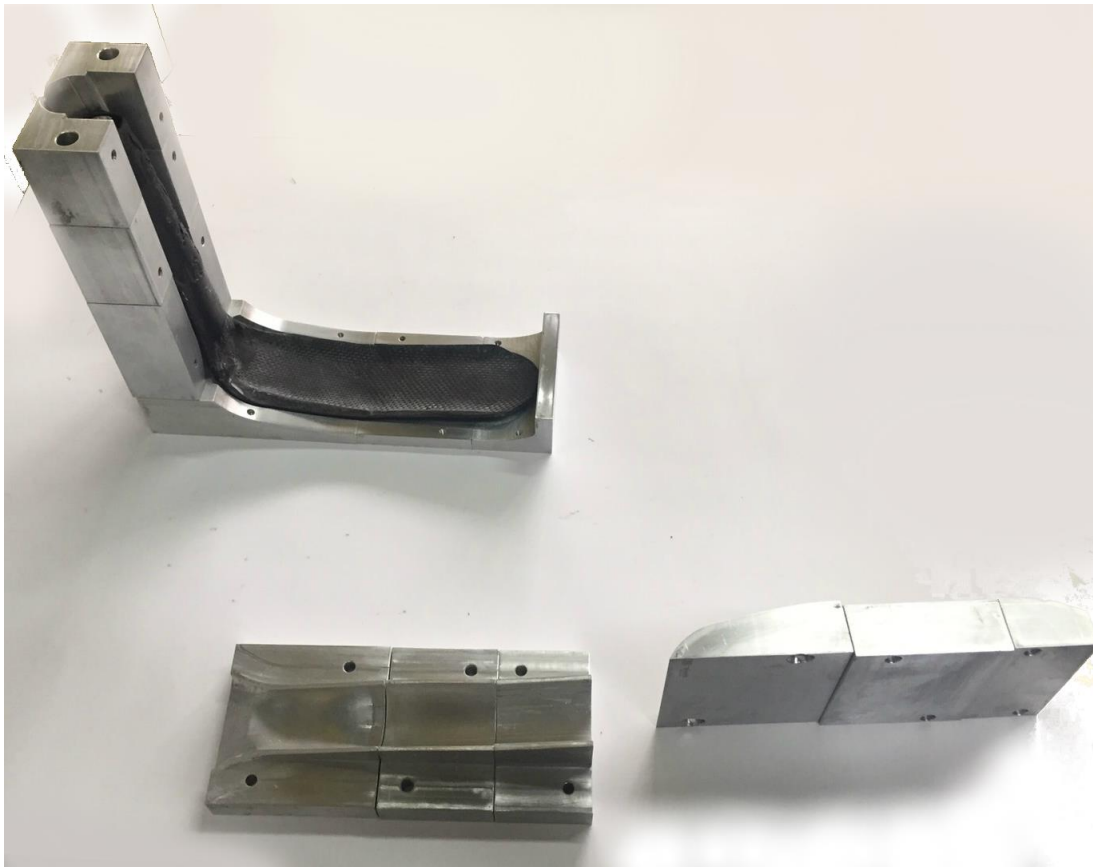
Molde superior con las contrapartes retiradas al momento de desmoldeo
